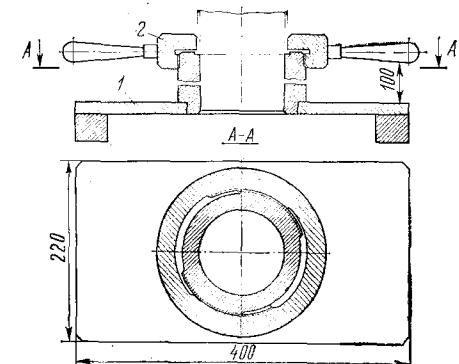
Приспособление для зажима гильзы цилиндров при хонинговании:
